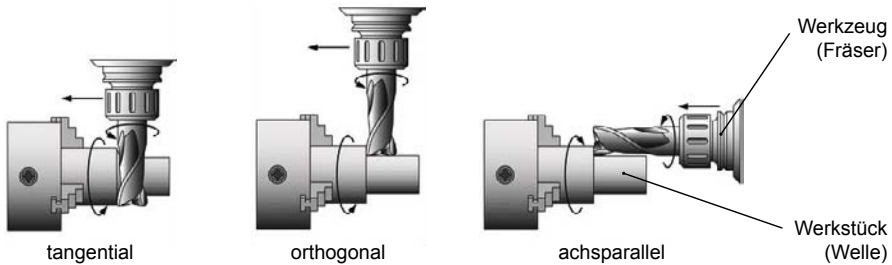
Mögliche Werkzeug-Werkstückanordnungen beim Drehfräsen [122]
